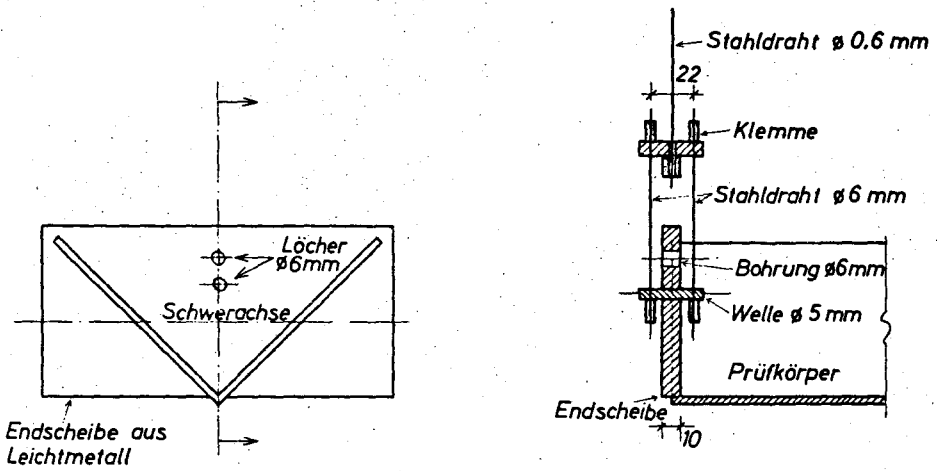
Aufhängevorrichtung für Prüfkörper mit Endscheiben
